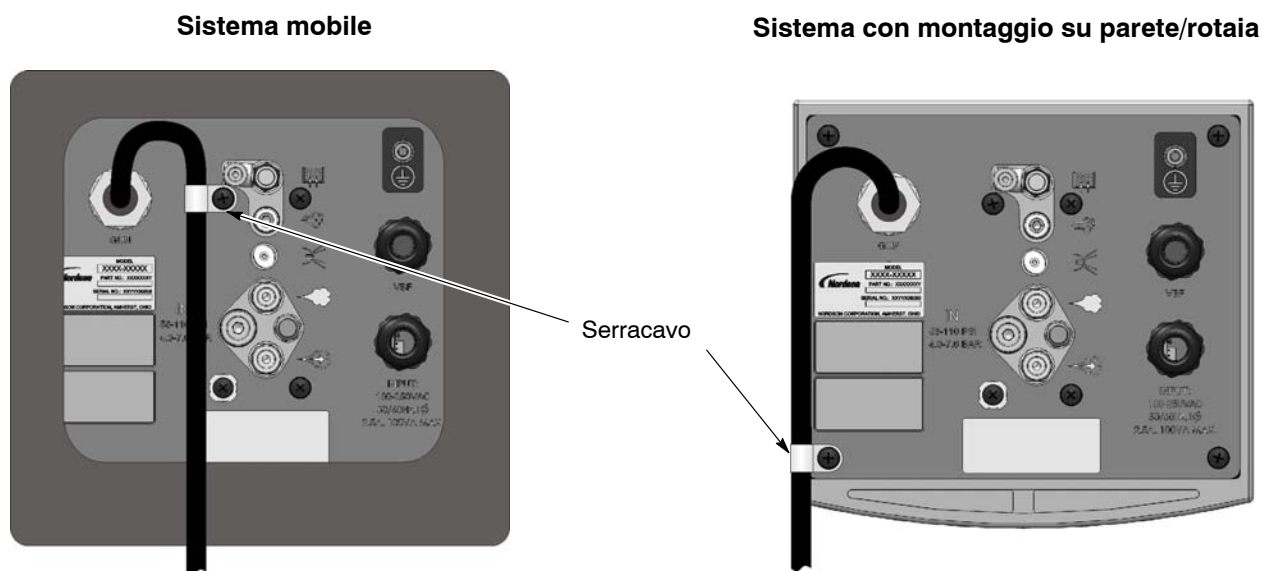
Collegamento del cavo della pistola e montaggio del serracavo
